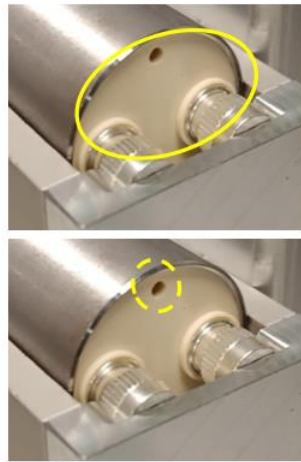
Orificio del switch colocado correctamente en el nido.
